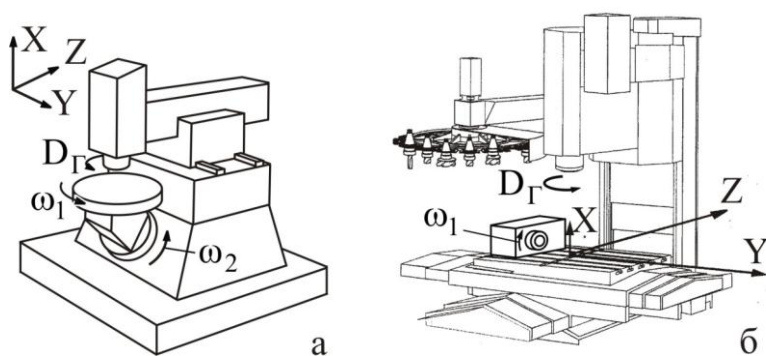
Станки, пригодные для обработки зубчатых колес ОСКГП
